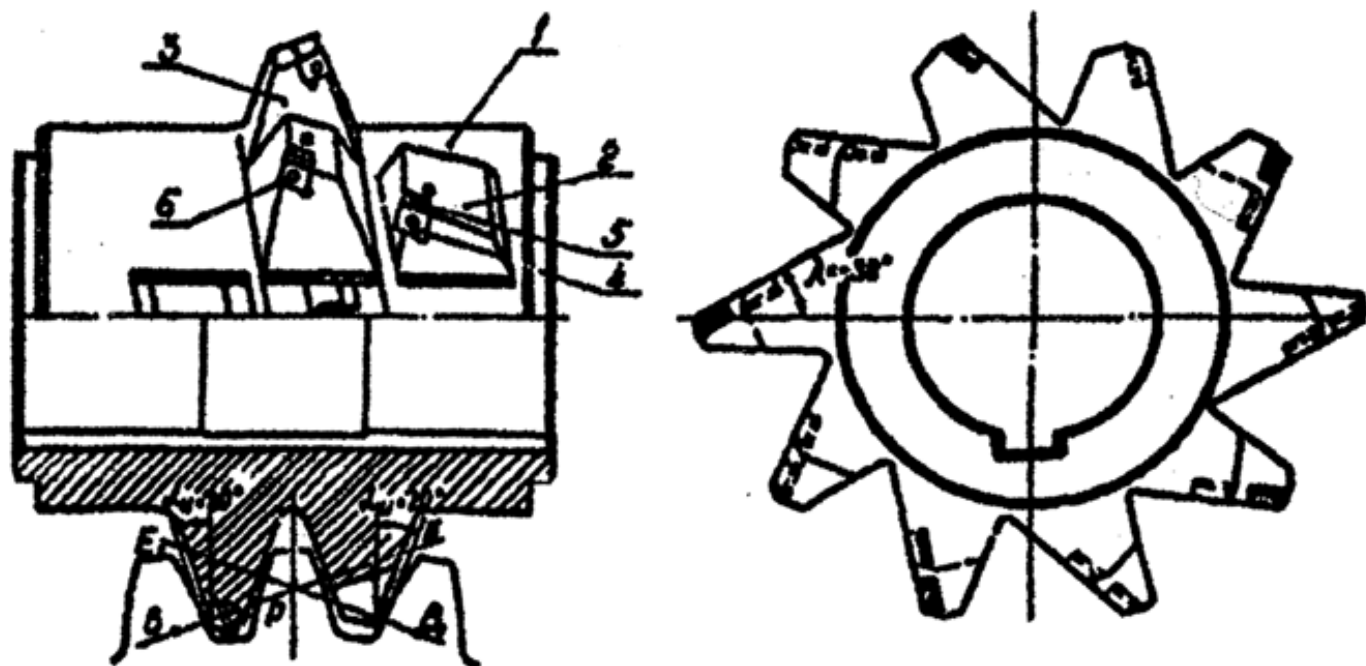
Червячная фреза с коническими зубчатыми выступами.
